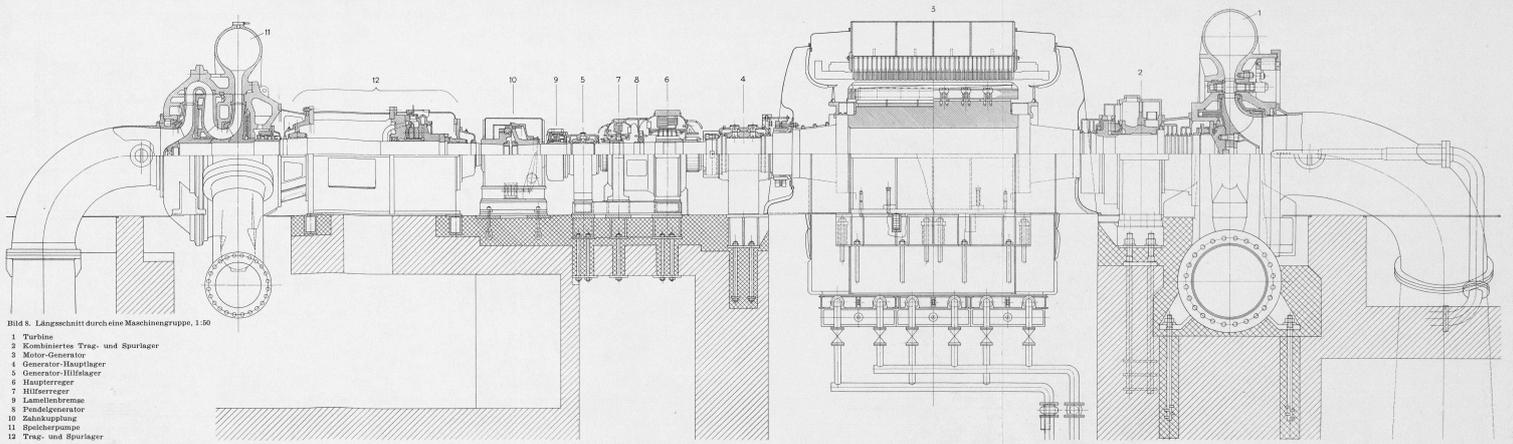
Längsschnitt durch eine Maschinengruppe, 1:50
